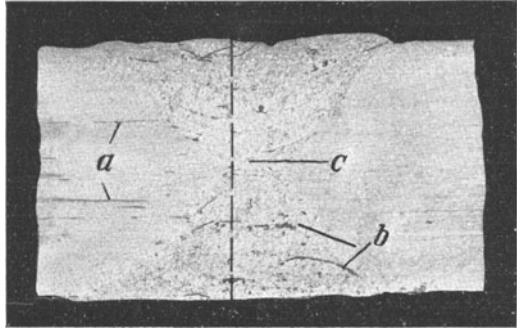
Starkes, doppelseitig geschweißtes Flußeisenblech mit Schlackeneinschlüssen.
